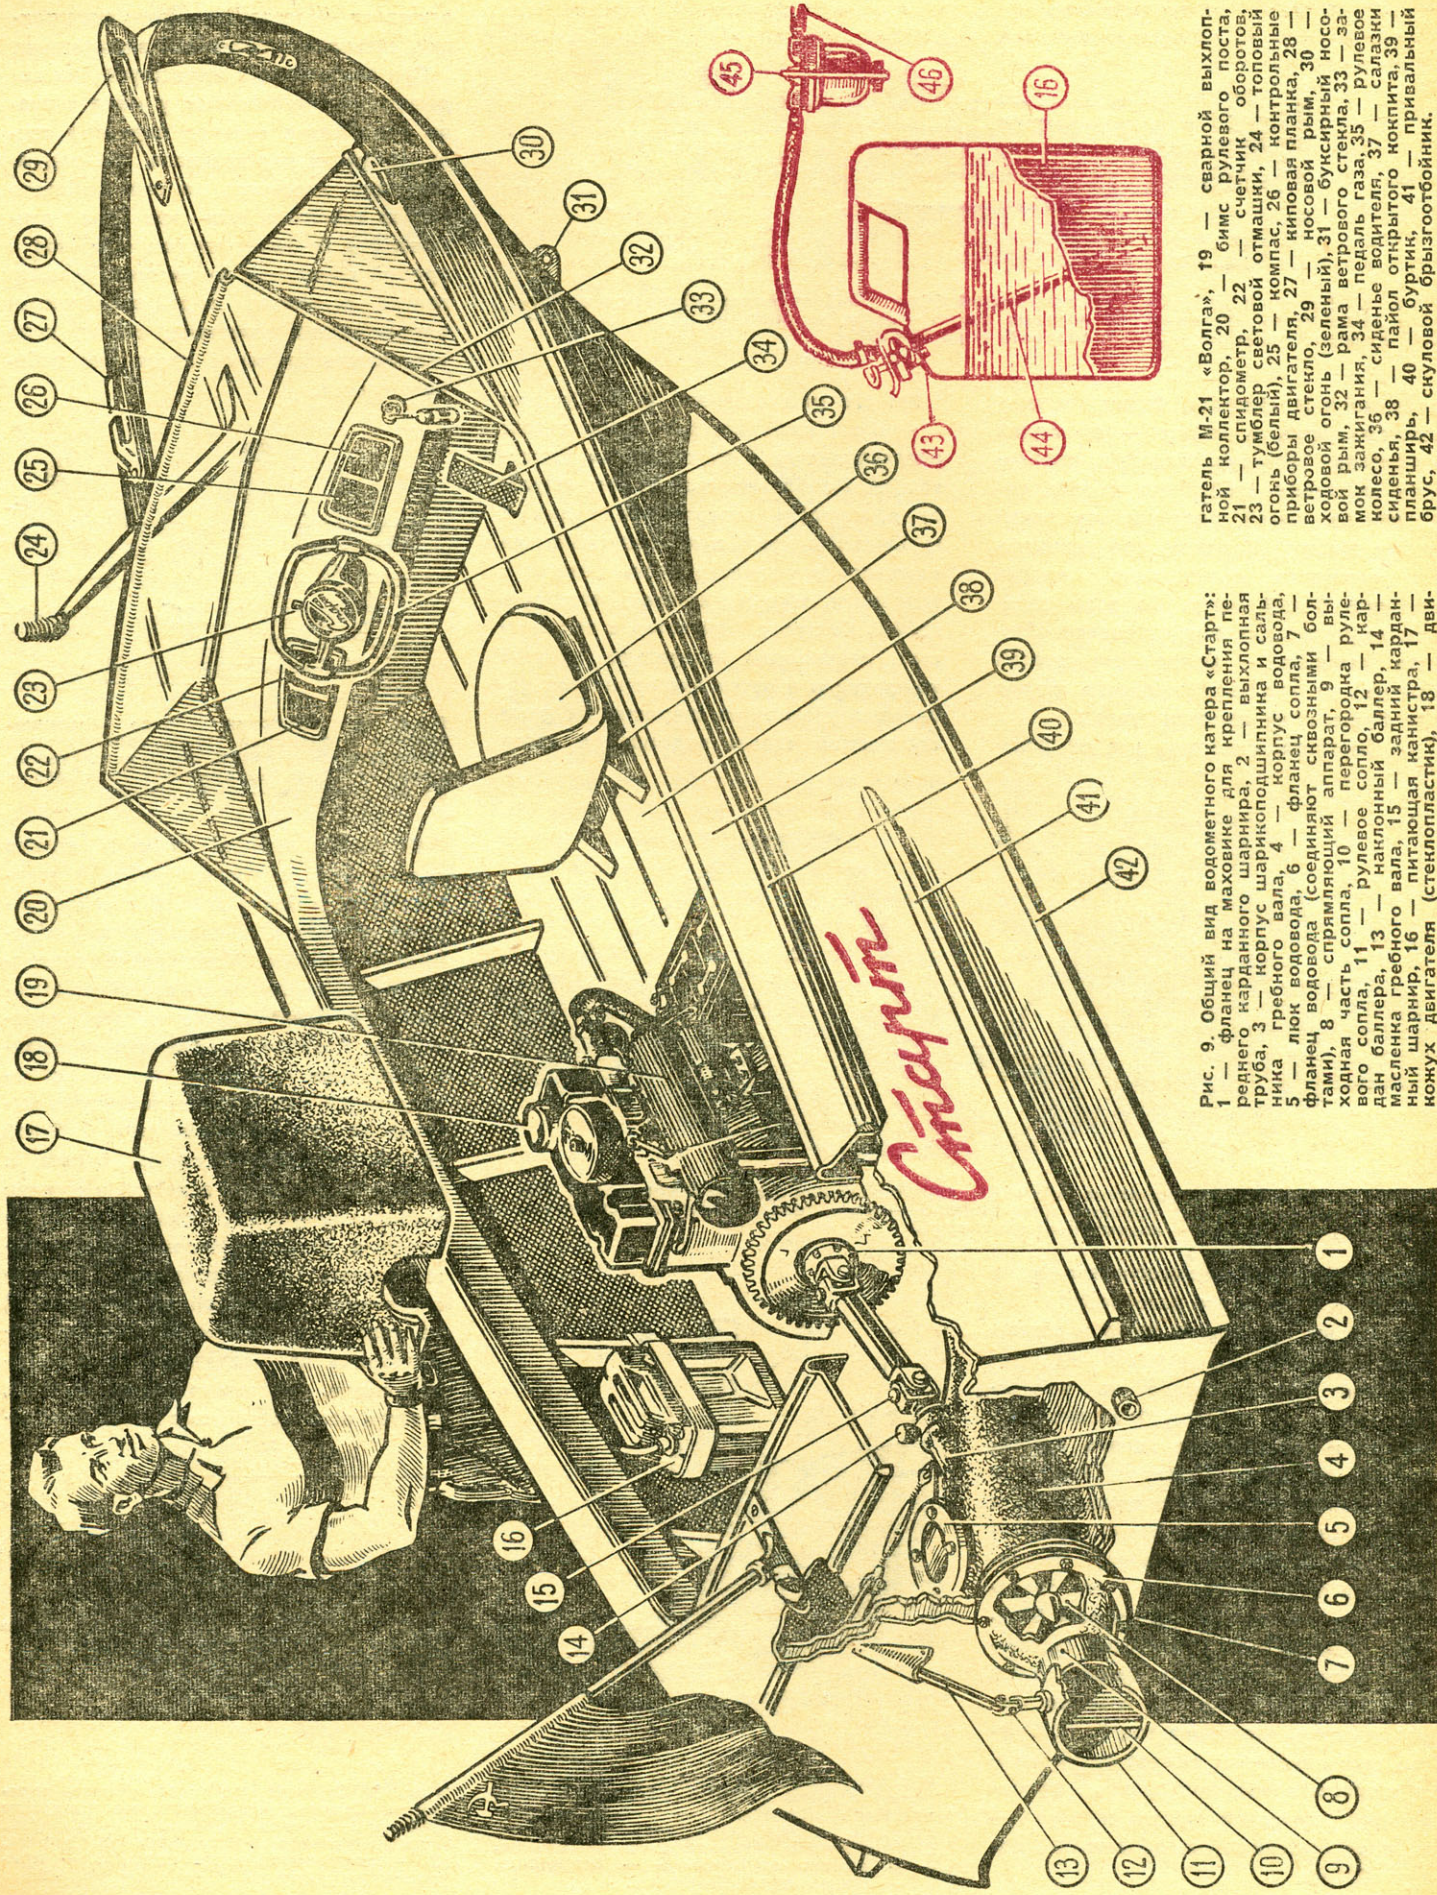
Общий вид водометного катера «Старт»: 1 — фланец на маховике для крепления переднего карданного шарнира, 2 — выхлопная труба, 3 — корпус шарикоподшипника и сальника гребного вала, 4 — корпус водовода, 5 — люк водовода, 6 — фланец сопла, 7 — фланец водовода (соединяют сквозными болтами), 8 — спиральный аппарат, 9 — выходная часть сопла, 10 — перегородка рулевого сопла, 11 — рулевое сопло, 12 — кардан баллера, 13 — наклонный баллер, 14 — маслянка гребного вала, 15 — задний карданный шарнир, 16 — питающая канистра, 17 — кожух двигателя (стеклопластик), 18 — дви-
